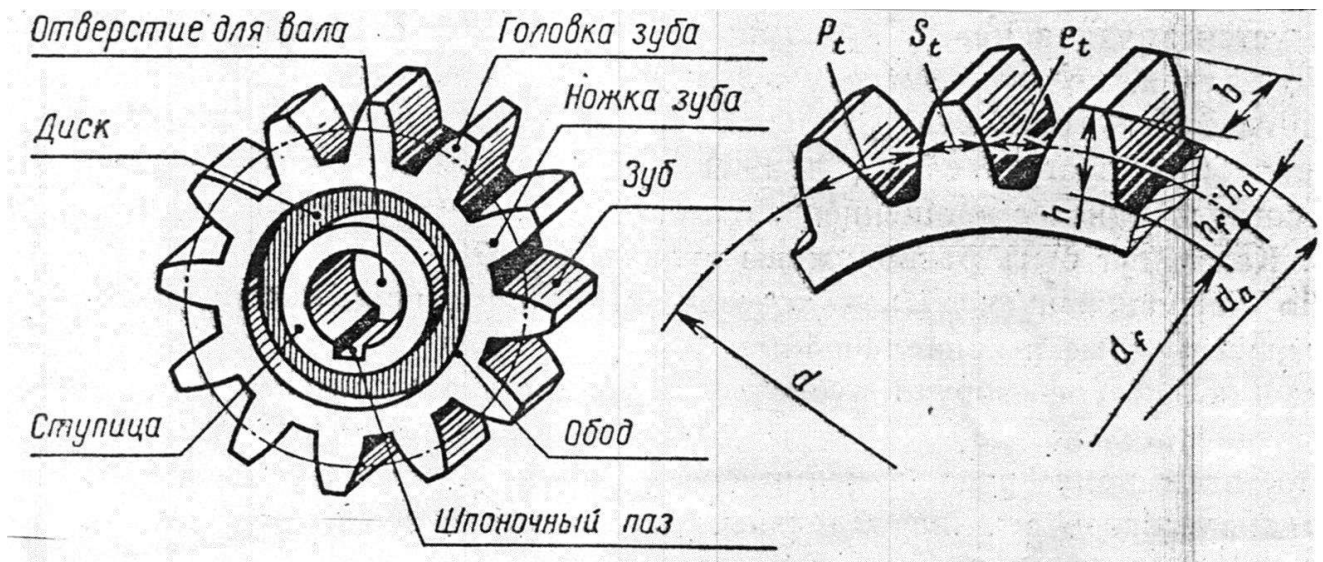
Зубчатое колесо с эвольвентным профилем зуба
